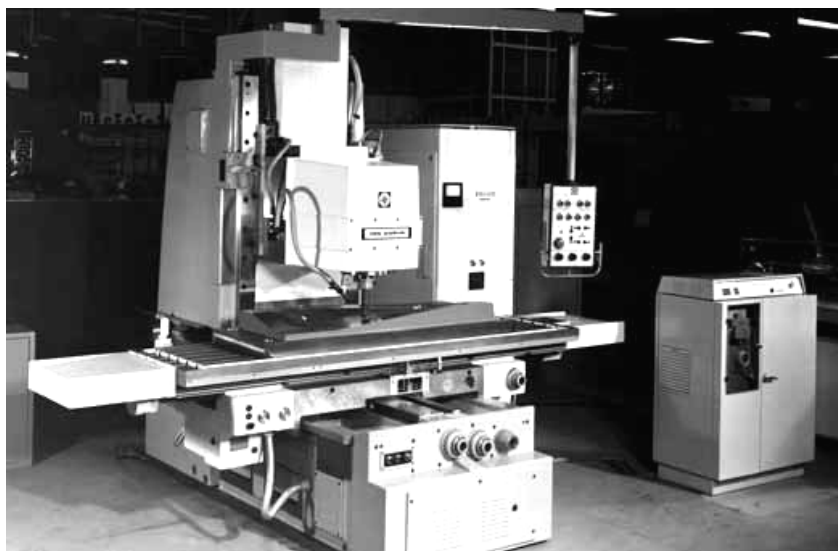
Univerzální konzolová frézka FB. ¹⁴
